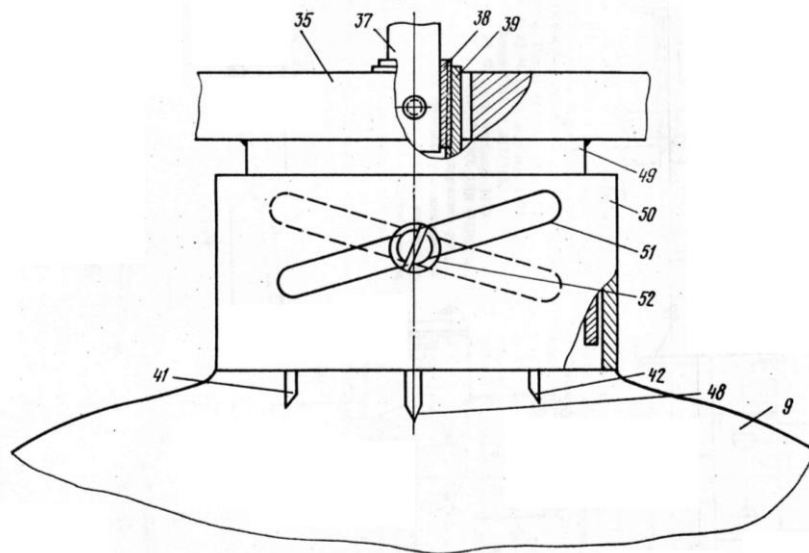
Регулятор глибини надрізу листків головки капусти
